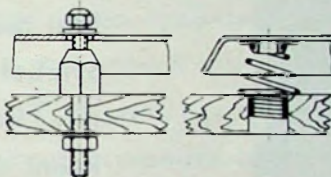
Befestigung des Chassis auf dem Werkboden. Links: Transportzustand; rechts: Betriebszustand
